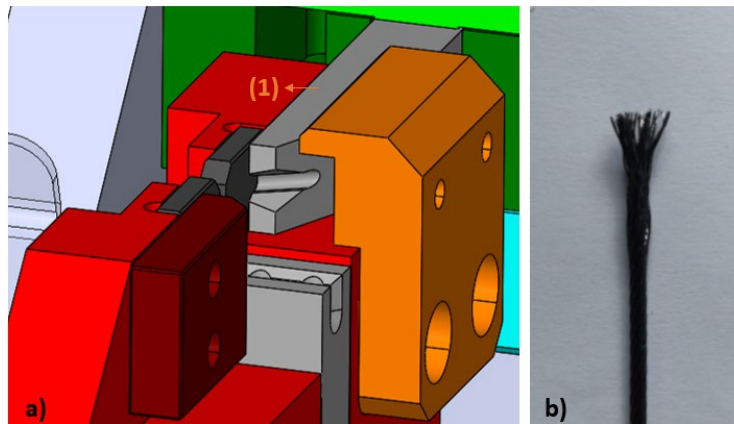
a) Sistema corte mecânico; (1) – Lâmina corte mecânico; b) – Cabo destrançado
